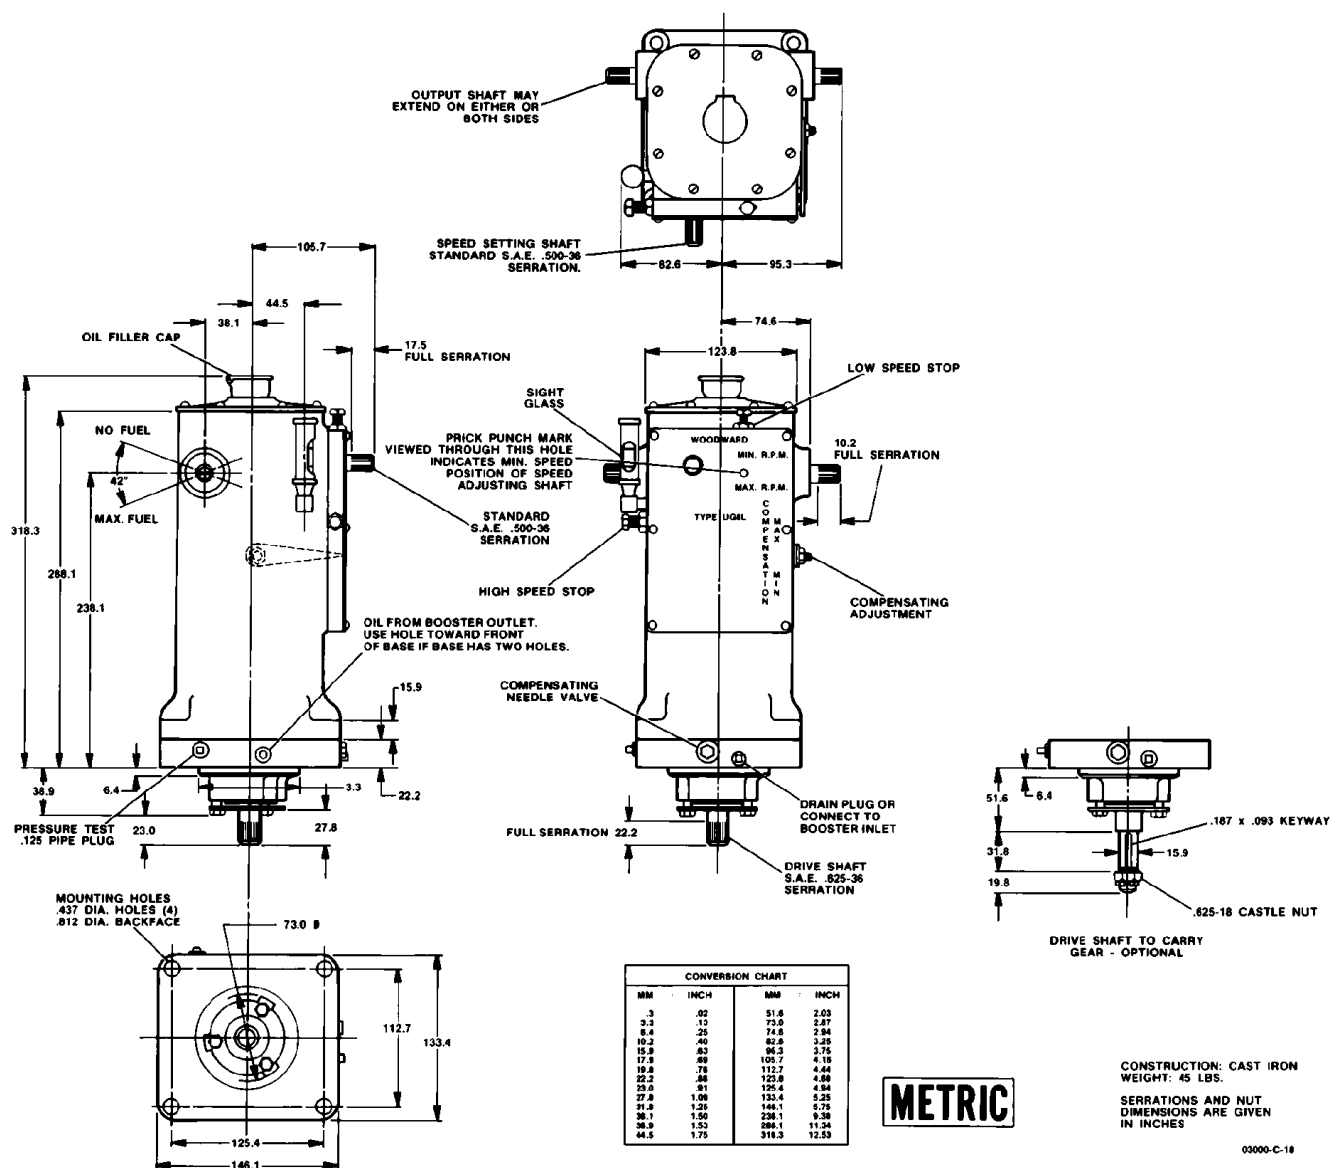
Dibujo del exterior del gobernador de palanca UG
